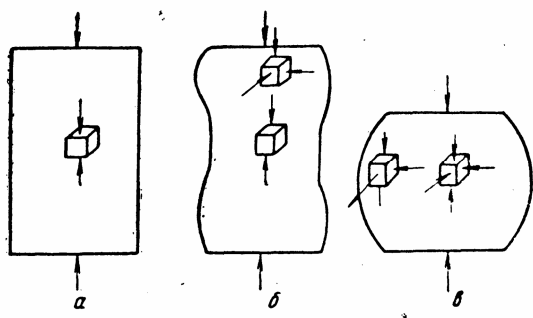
Схеми напружень при осіданні циліндричних заготовок:
